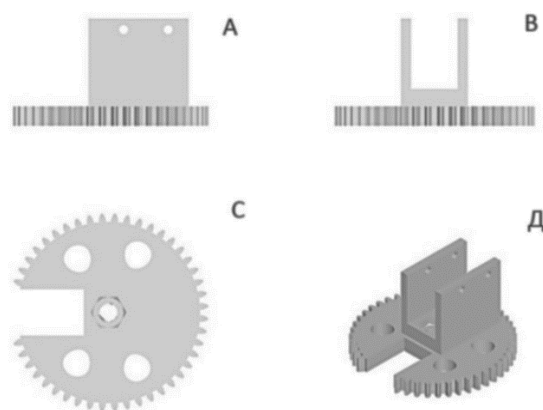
Шестерня ноги: А – вид спереди; В – вид слева; С – вид сверху; Д – общий вид
